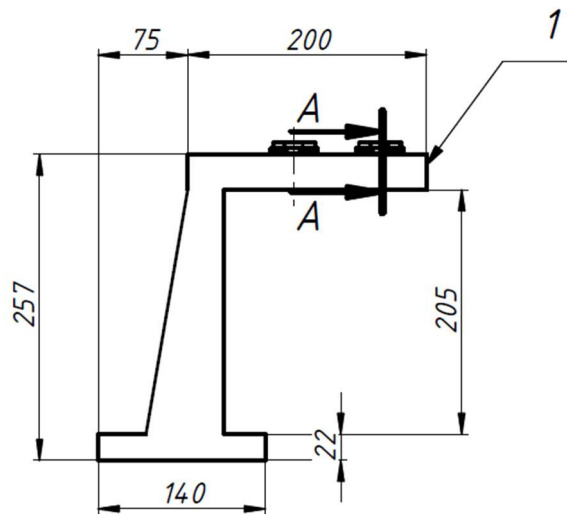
Кондуктор зі змінними втулками (Вид 1)
